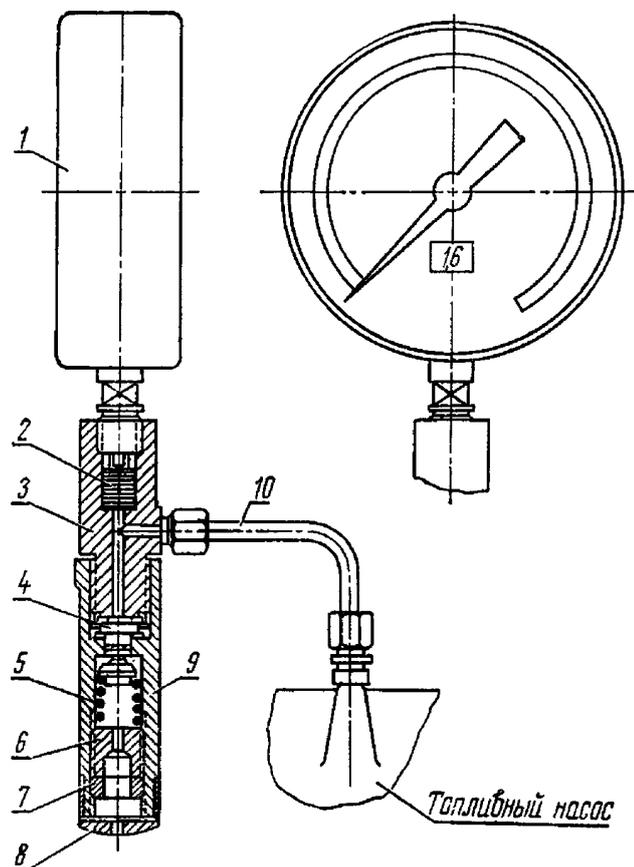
Прибор КИ-4802М для проверки состояния прецизионных пар топливного насоса: 1 — манометр; 2 — дроссельные шайбы; 3 — корпус; 4 — предохранительный клапан; 5 — пружина клапана; 6 — регулировочная гайка; 7 — контргайка; 8 — защитный колпак; 9 — рукоятка; 10 — топливопровод.
